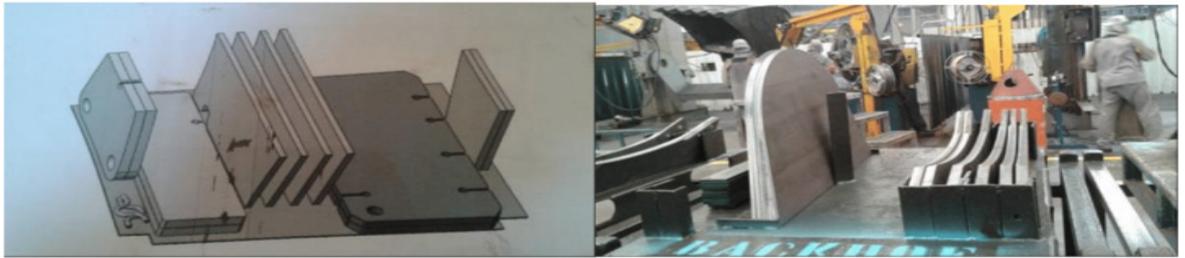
Kits de abastecimento projetado e construído (real) para disposição da matéria prima no setor.
